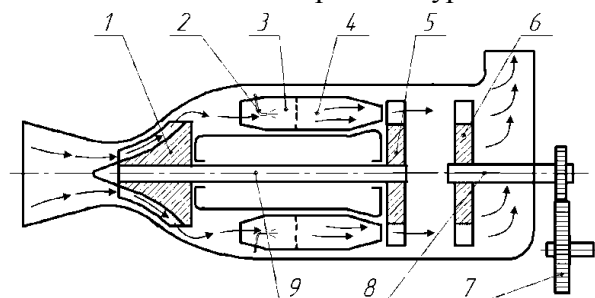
Схема двовального газотурбінного двигуна (ГТД): 1 – компресор відцентровий; 2 – форсунка; 3 – камера згорання; 4 – камера змішування; 5
